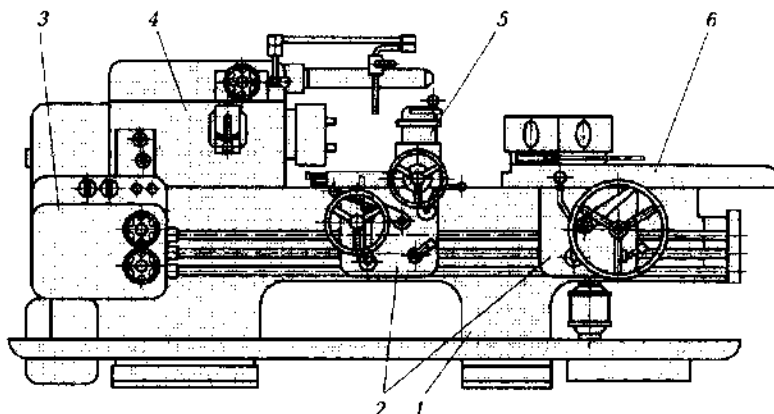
Токарно-револьверный станок модели 1П365:
